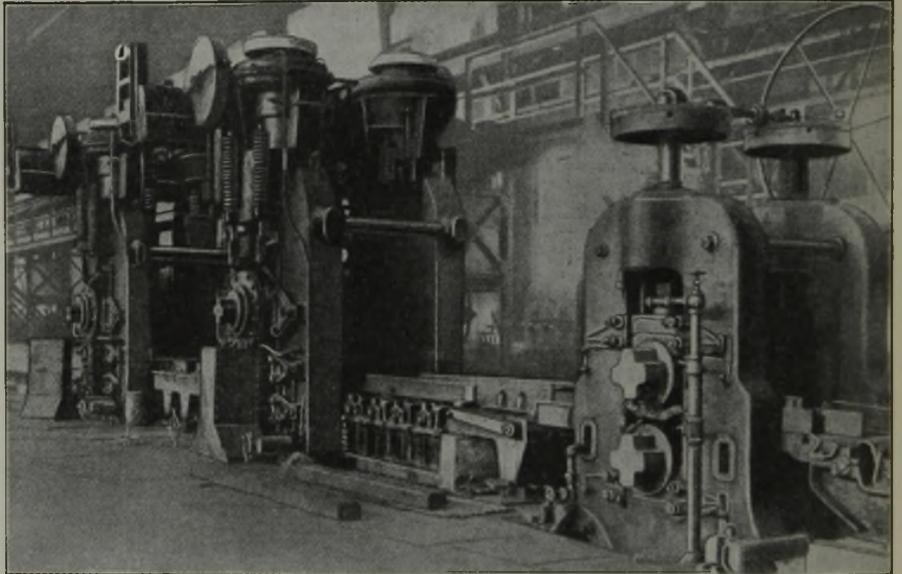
5. Vorgerüst, 1. und 2. Fertiggerüst.
